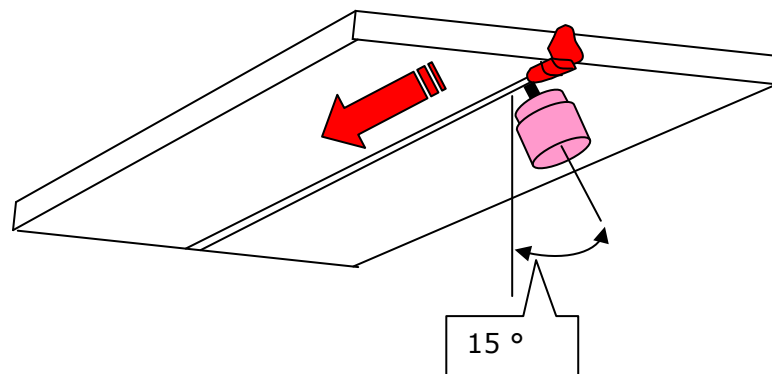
Realización de la soldadura de placas a tope, en posición sobre cabeza, sin aporte.
